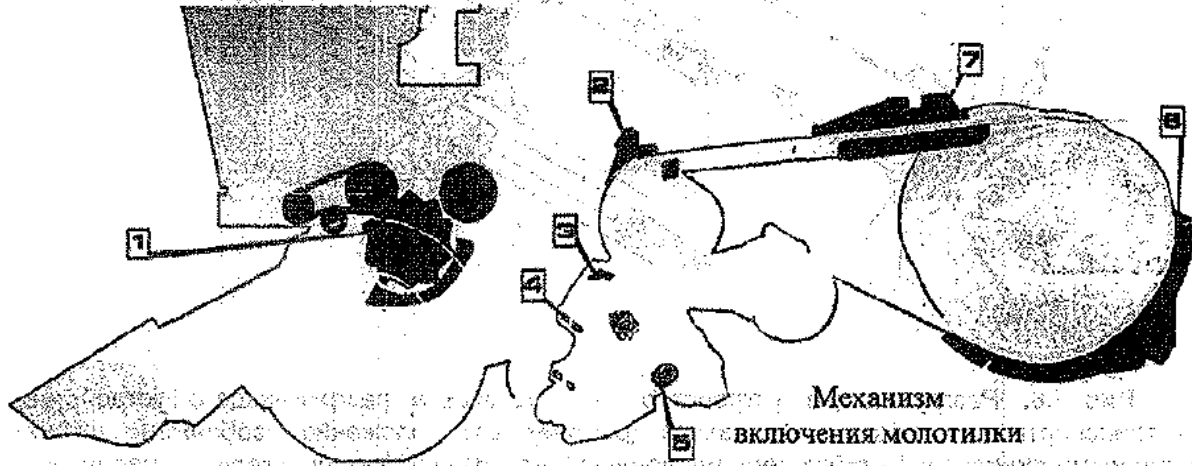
Схема регулировки молотильного устройства и механизма включения молотилки: 1- молотильное устройство; 2-палец подъемника; 3-подъемник; 4-боковина кронштейна; 5-пружина; 6-нижний кожух; 7-верхний кожух.
